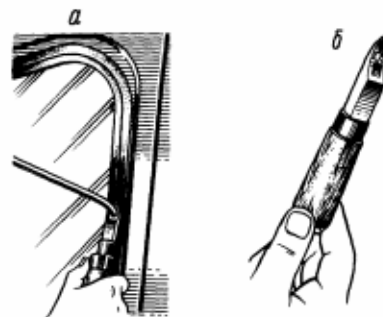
Установка замочного вкладыша при помощи оправки:
